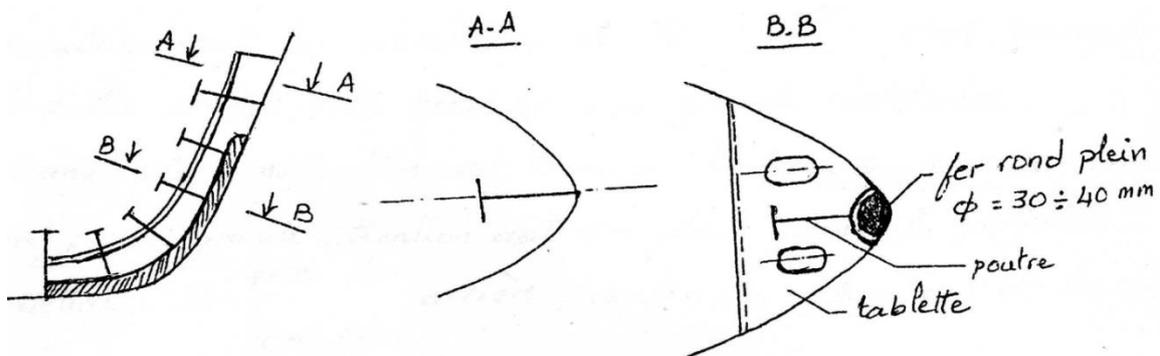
L'étrave renforcée par fer plat et une poutre.
